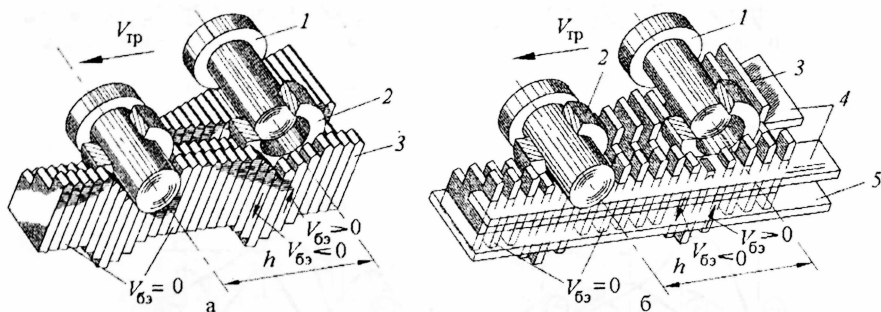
Непрерывная сборка изделий в кинематических призмах: а - базирование сопрягаемых деталей подвижными БЭ; б - базирование сопрягаемых деталей подвижными и неподвижными БЭ
